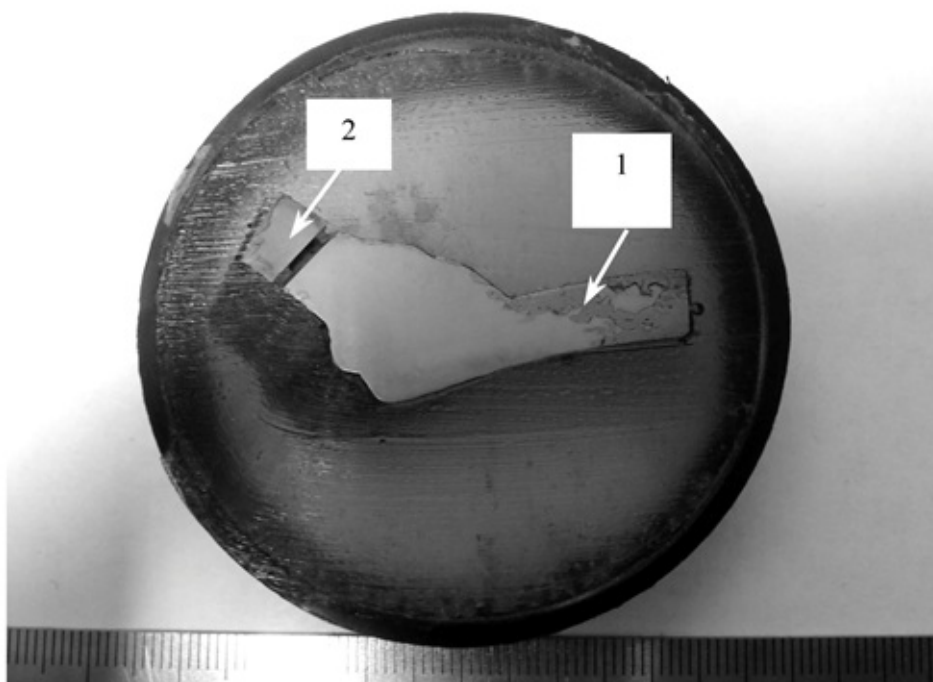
Внешний вид темплета №1 сварного шва узла врезки:
